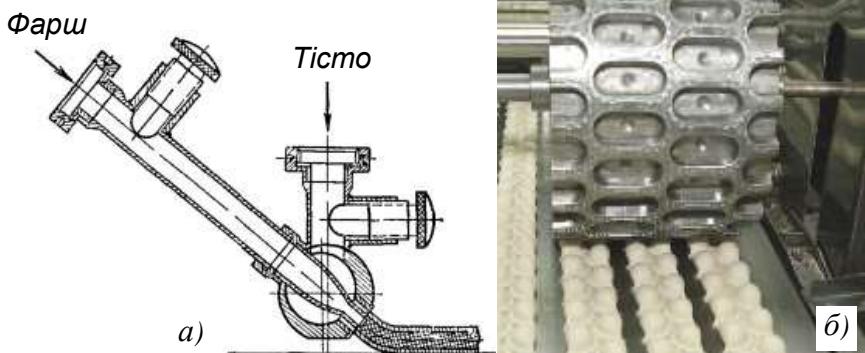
Формувальний пристрій а) і штампувальний барабан б).
